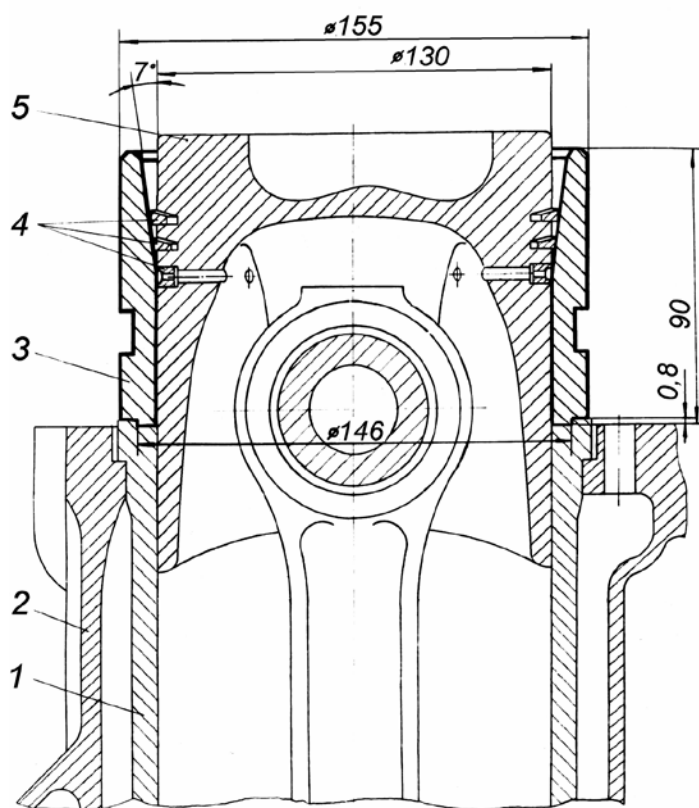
Оправка для установки поршня в гильзу цилиндра
